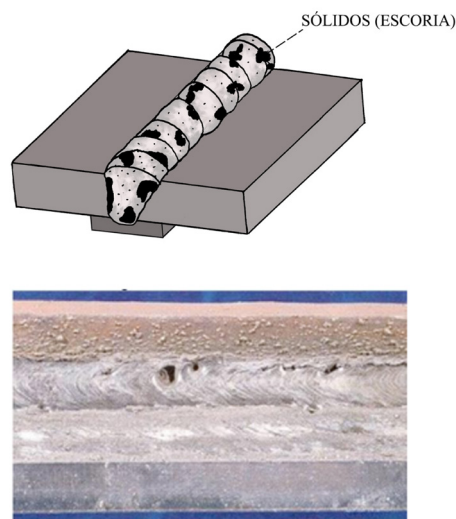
Defectos en la soldadura: Inclusiones sólidas
